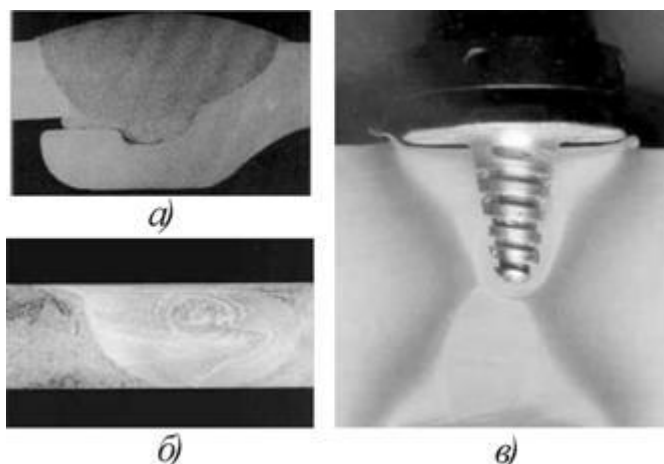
Макроструктуры швов полученных сваркой плавлением (а), ПСТ (б) и двухсторонняя сварка (в).
